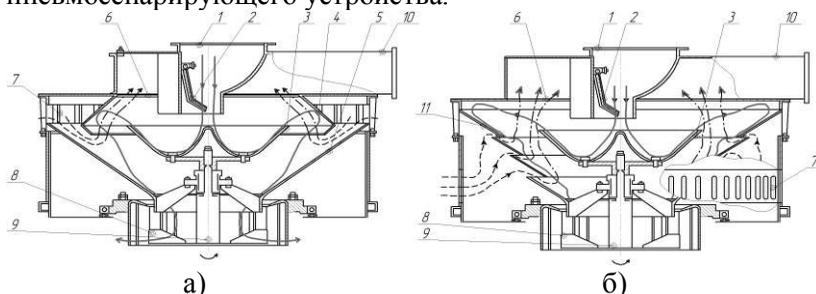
Серийное а) и разработанное б) пневмосепарирующие устройства: 1 – патрубок загрузочный; 2 – клапан; 3,8 – разбрасыватели; 4 – отражатель; 5 – конус; 6 – диафрагма; 7 – воздухозаборники; 9 – вал; 10 – патрубок отводной; 11 – конус каскадный; - - - - - движение воздушного потока; ······ – легких примесей; ——— – зерновой смеси
